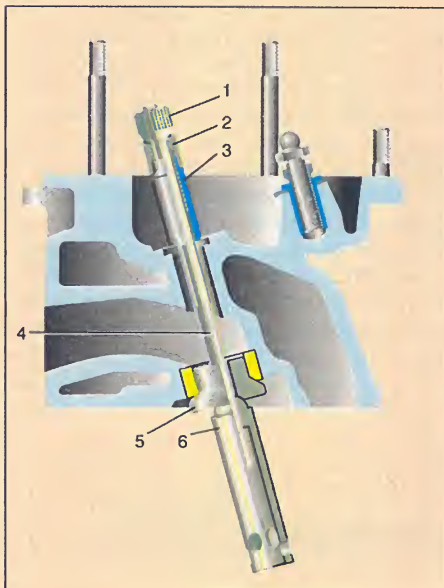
Запрессовка направляющей втулки клапана без применения ударов: 1 – гайка верхняя; 2 – оправка; 3 – направляющая втулка; 4 – шпилька; 5 – упор в седло клапана; 6 – гайка нижняя.
